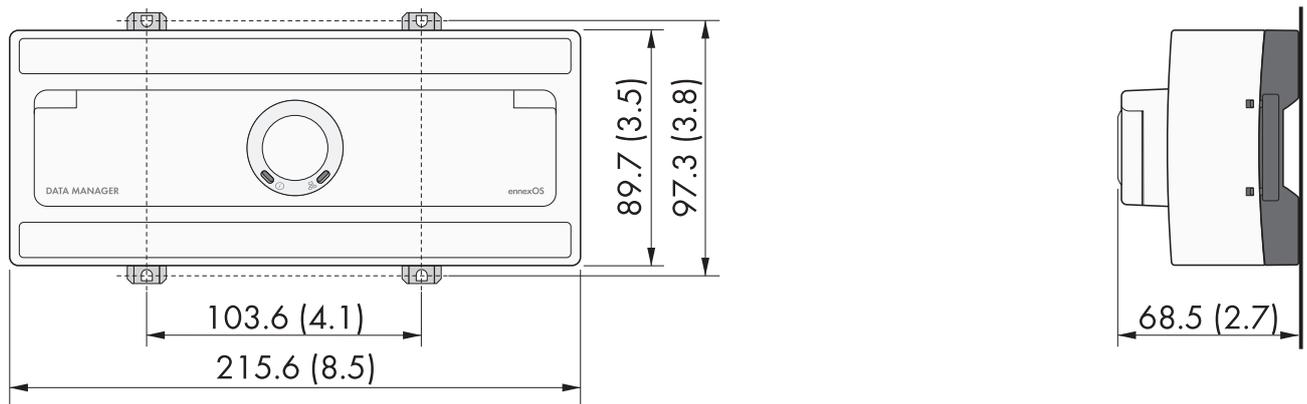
Dimensioni per il montaggio a parete (in mm (in))
